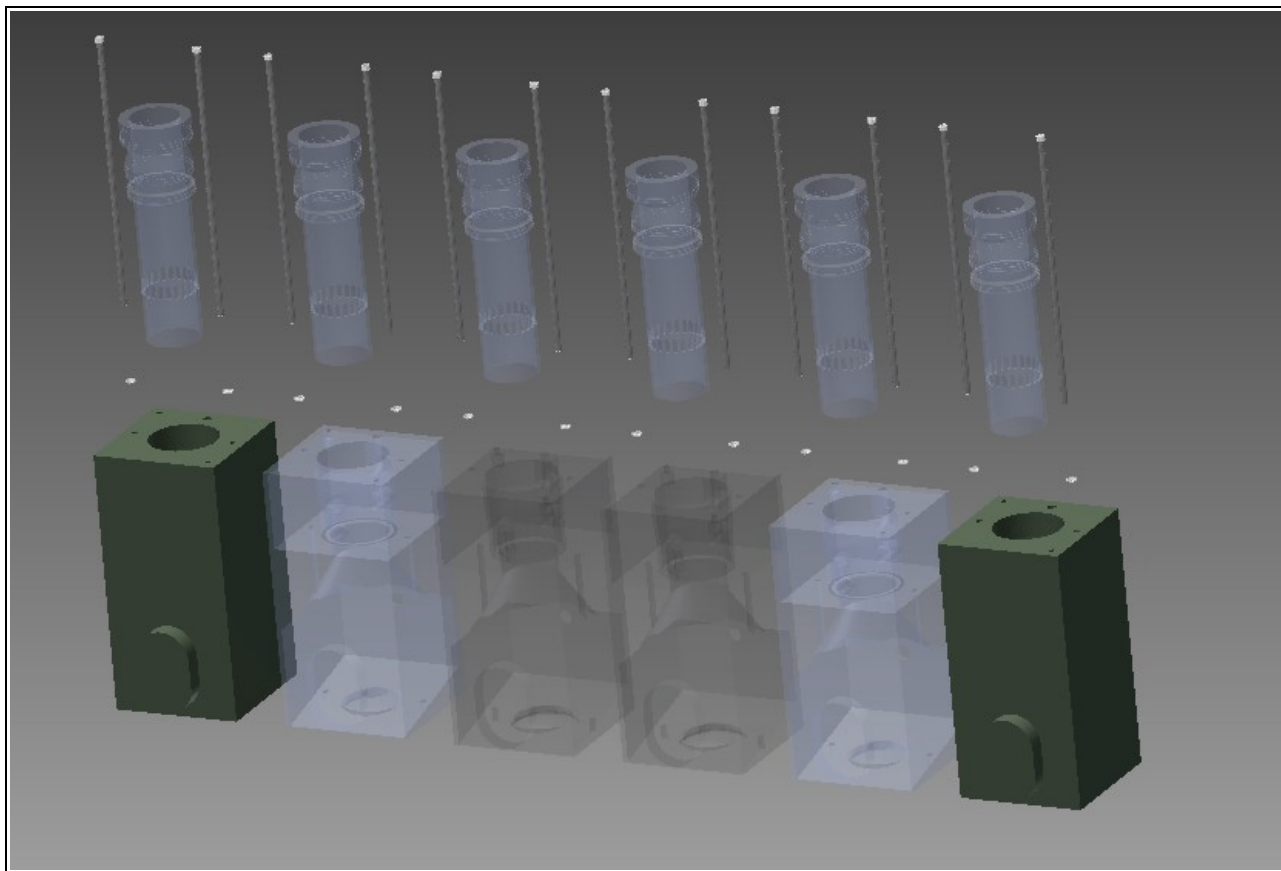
Bloque de cilindros, explosionado
